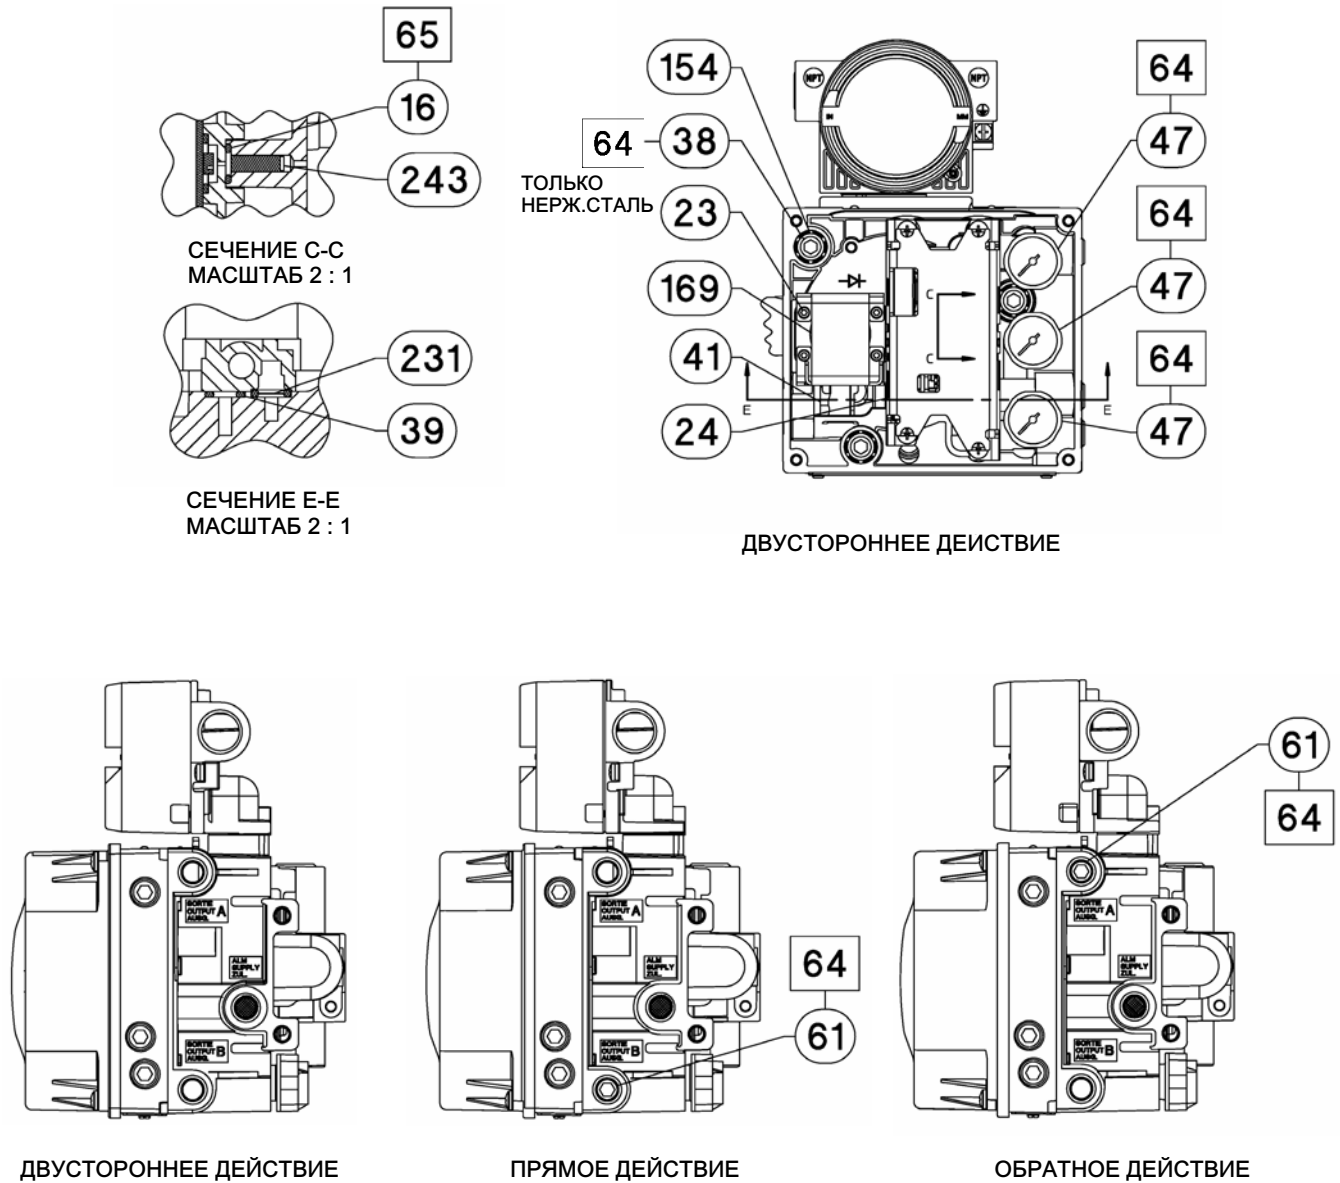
7. Корпус основного блока СПАЗ FIELDVUE DVC6205 в сборе (продолжение)
